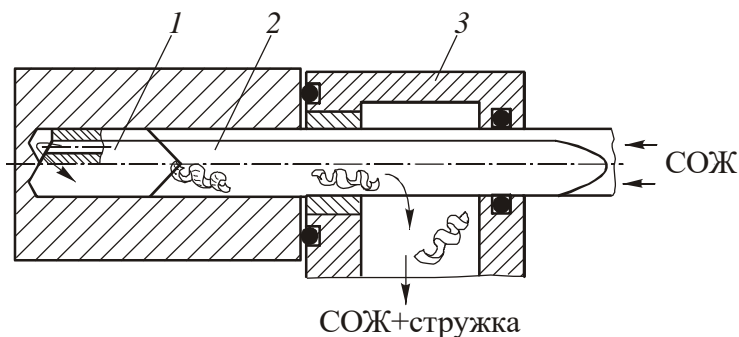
Схема обработки глубокого отверстия ружейным сверлом:
